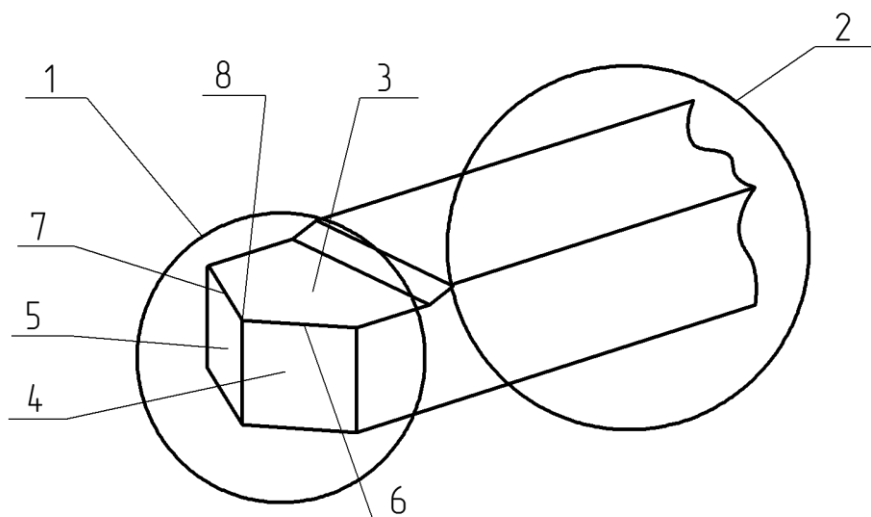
Конструктивные параметры токарного резца: 1 – лезвие резца; 2 – крепежная часть; 3 – передняя поверхность; 4 – главная задняя поверхность; 5 – вспомогательная задняя поверхность; 6 – главная режущая кромка; 7 – вспомогательная режущая кромка; 8 – вершина лезвия резца
